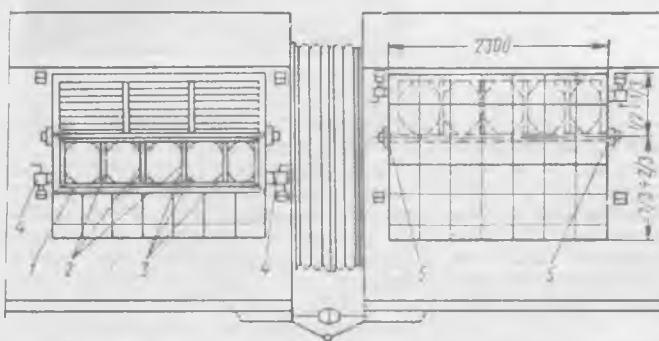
Схема зачехления секций холодильников тепловоза ТЭ3, предлагаемая работниками депо Смоленск: 1 — рамка; 2 — поперечная стойка; 3 — косынка; 4 — замковое устройство; 5 — шарнир
